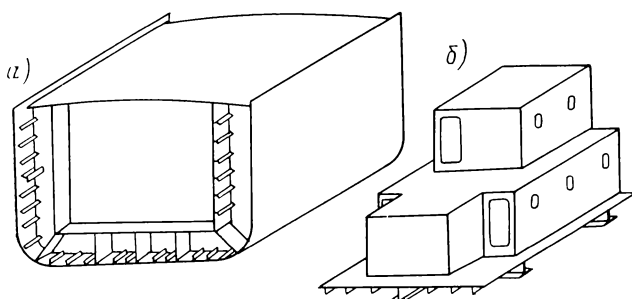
Блоки секций: а — корпуса; б — надстройки.
